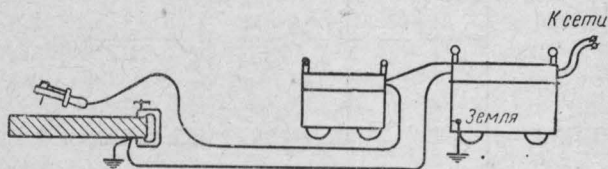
Схема заземления сварочного трансформатора.
